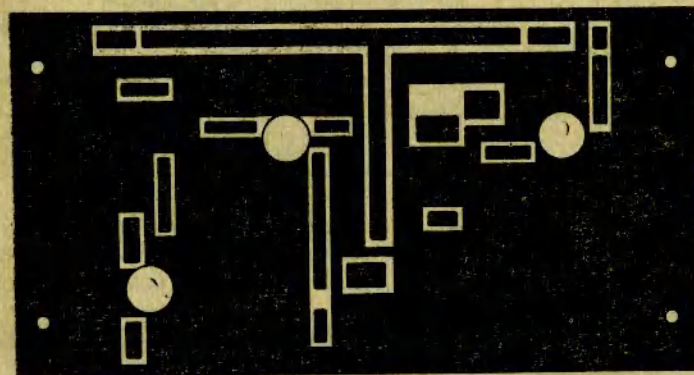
, б. Рисунок печатного монтажа платы конвертера
